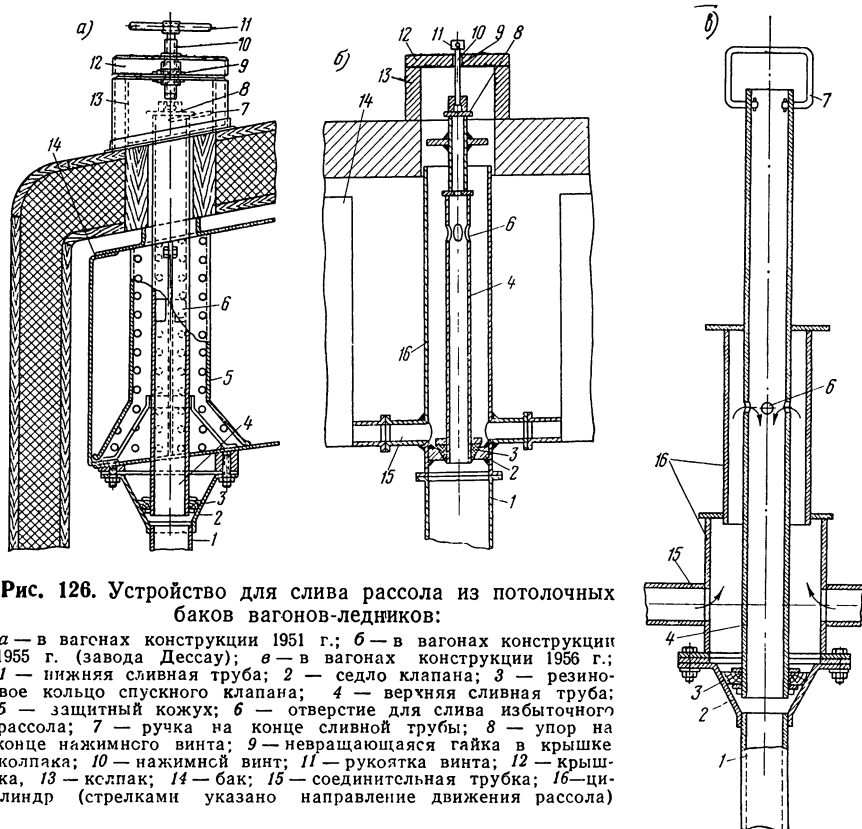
Устройство для слива рассола из потолочных баков вагонов-ледников:
